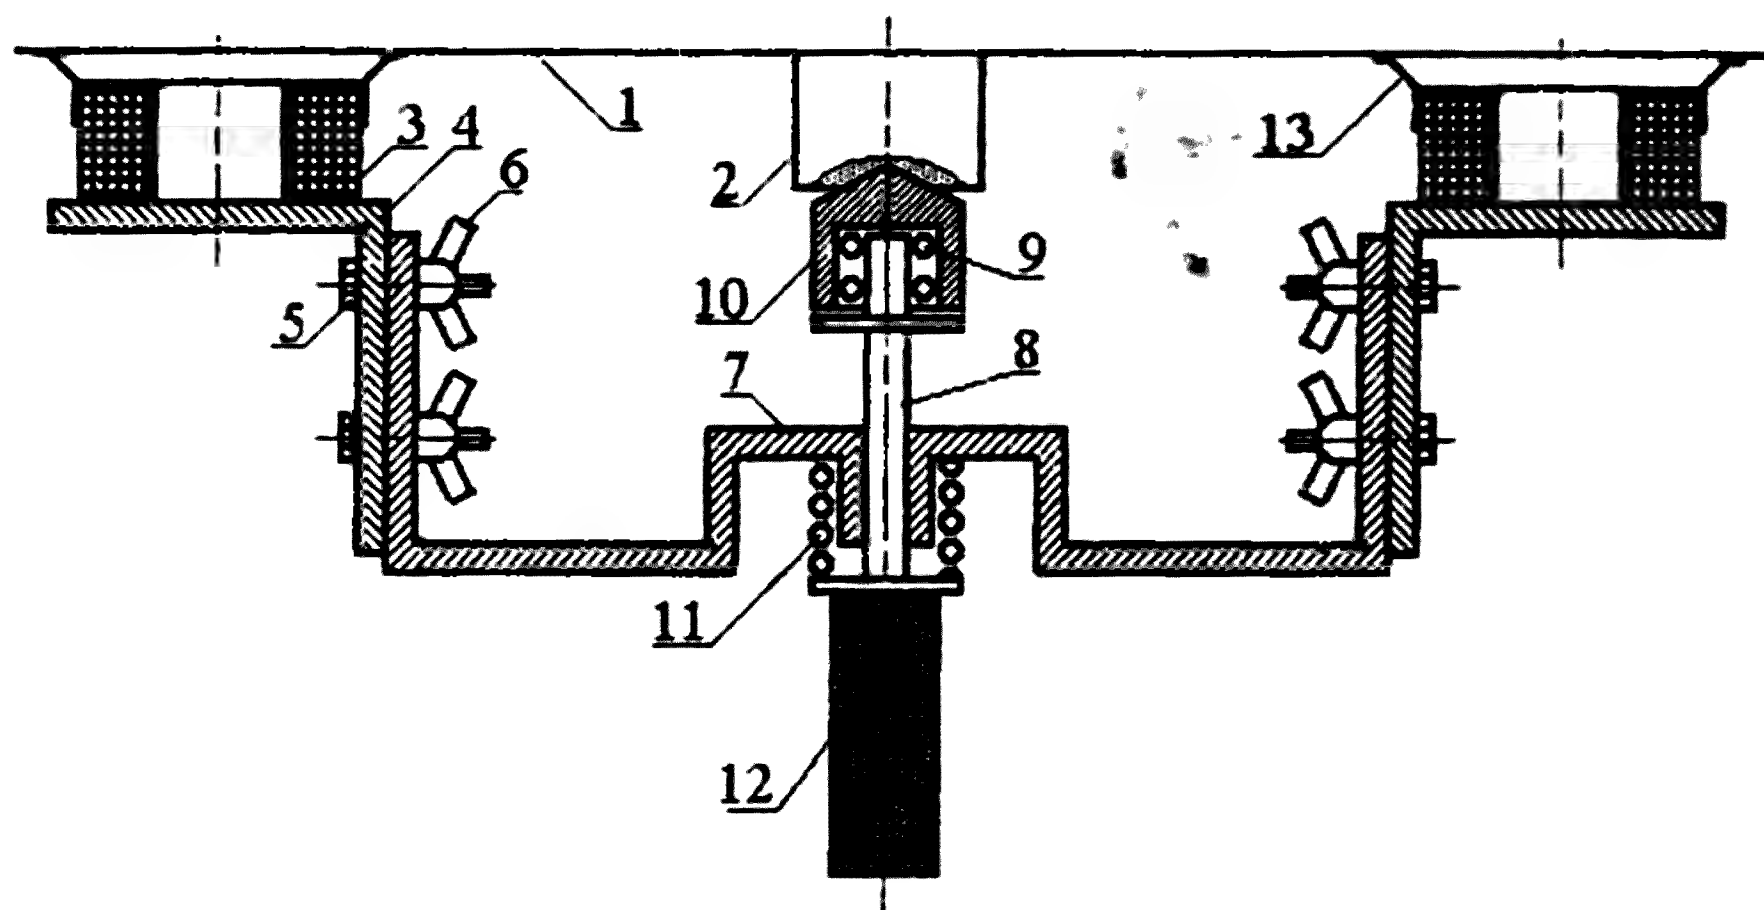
Конструкция измерительного щупа с двумя ТИП
